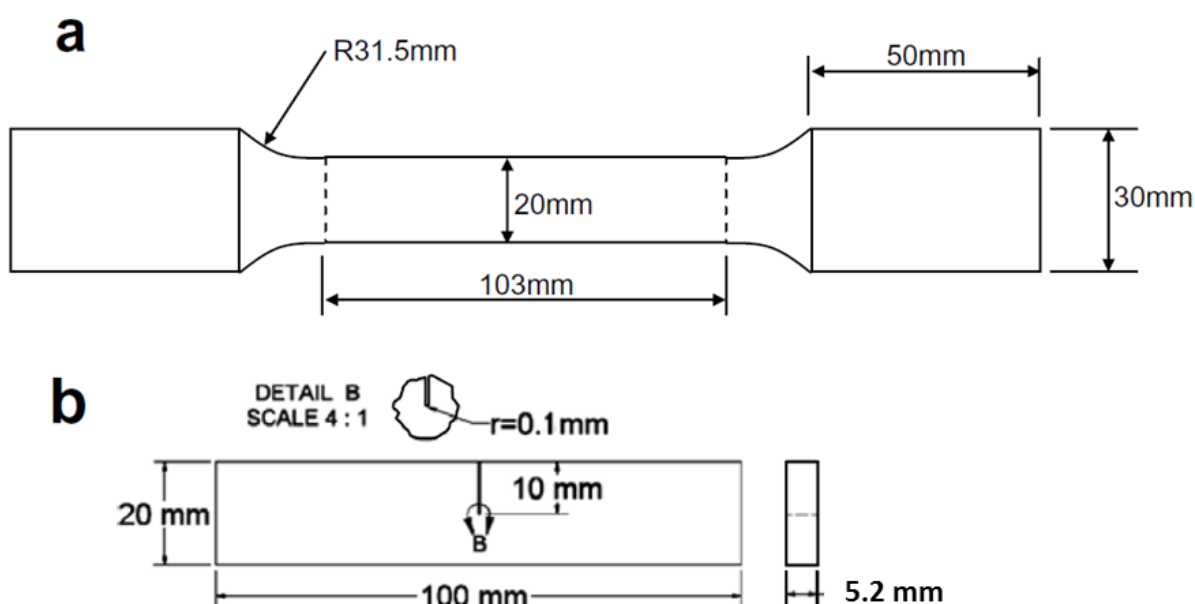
(a) Eprouvettes de fatigue. (b) éprouvettes de flexion découpées après le cumul de dommage par fatigue.
